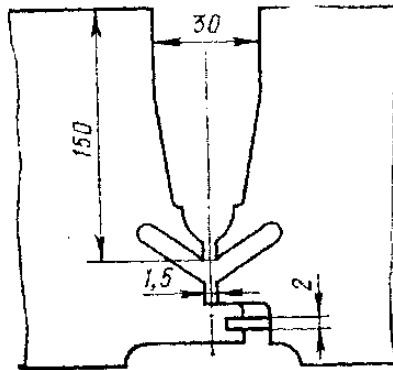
Конструкція стика кільцевого з'єднання вала ротора турбіни
